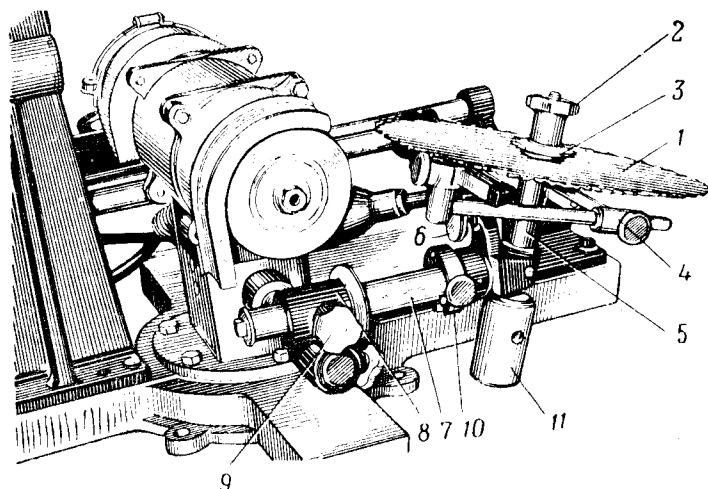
Механизм для заточки дисковых пил на станке И-121:
